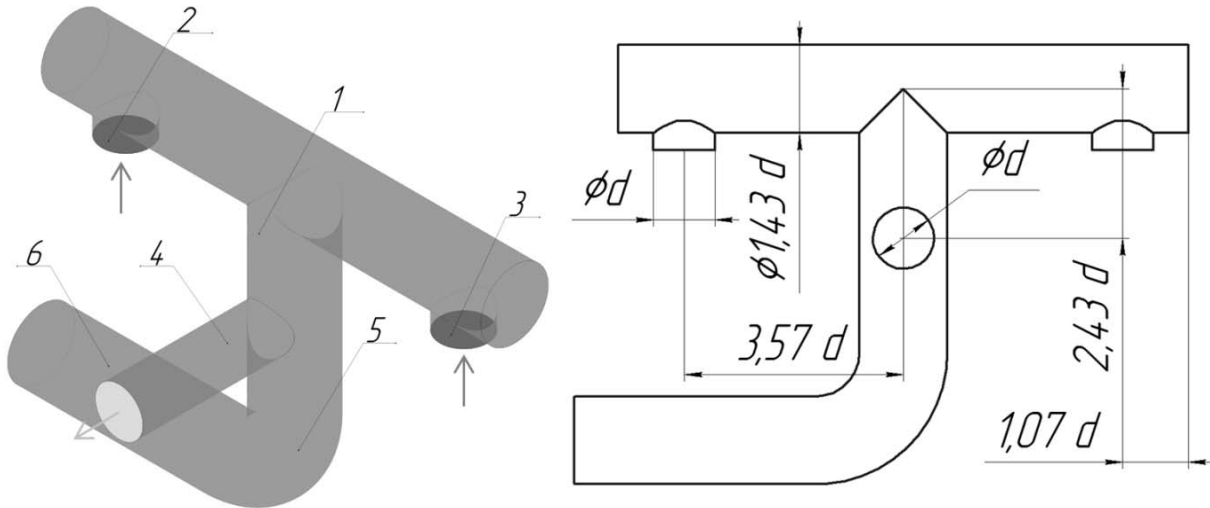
Общая схема коллектора (слева): 1 – напорный коллектор; 2,3 – подводы; 4 – боковой отвод; 5 – поворотное колено; 6 – общий отвод; основные размеры коллектора (справа)
